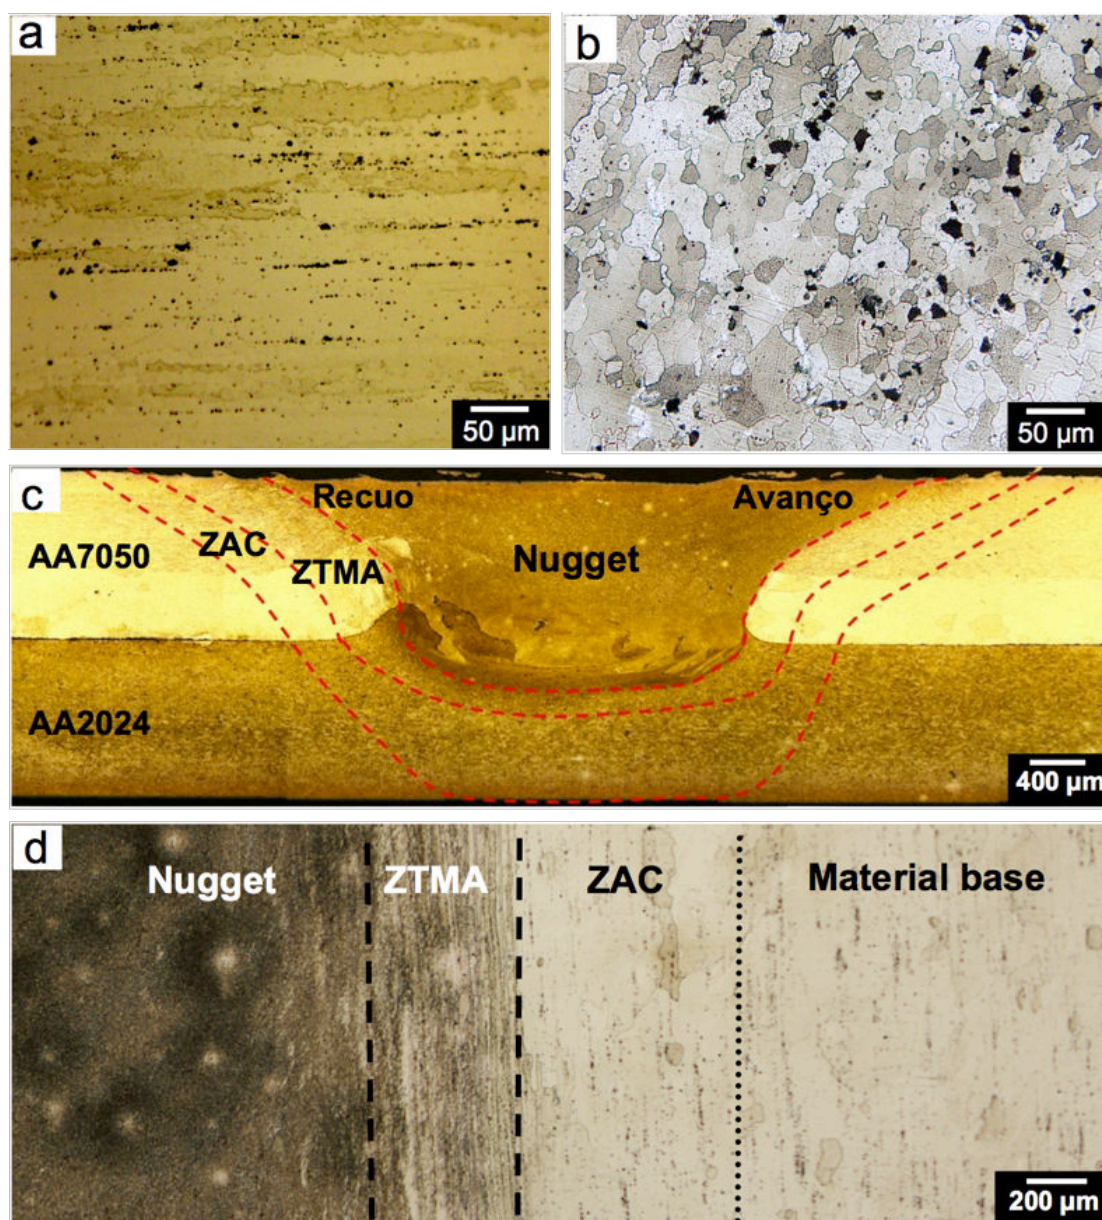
MO de (a) superfície da liga AA7050-T76511, (b) superfície da liga AA2024-T3, (c) seção transversal da solda FSW e (d) vista de topo da solda FSW. Amostras atacadas com reagente Keller.
